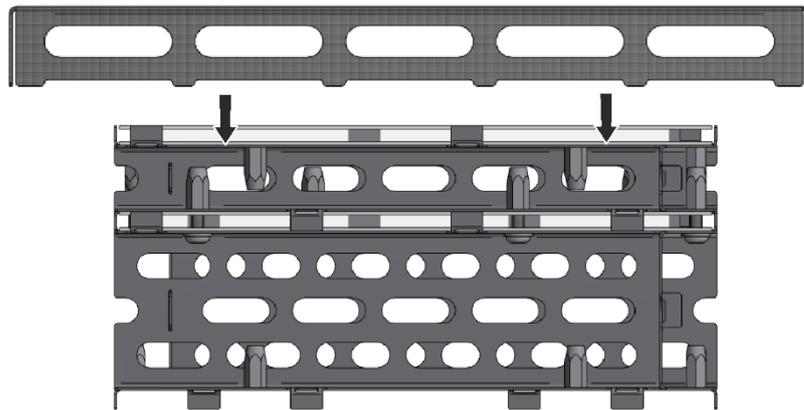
Poser et visser la vitre extérieure ainsi que l'écran frontal (figure similaire)
